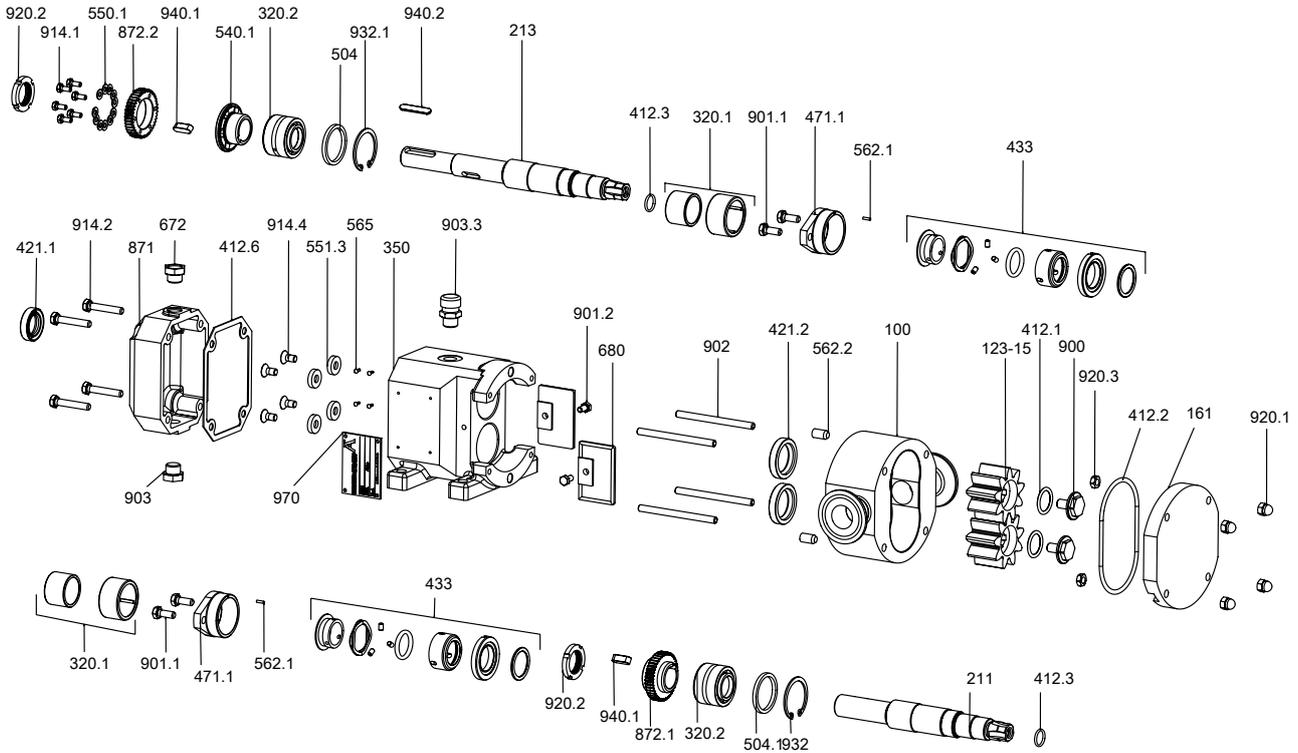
Explosionszeichnung Vitalobe Baugröße 100
